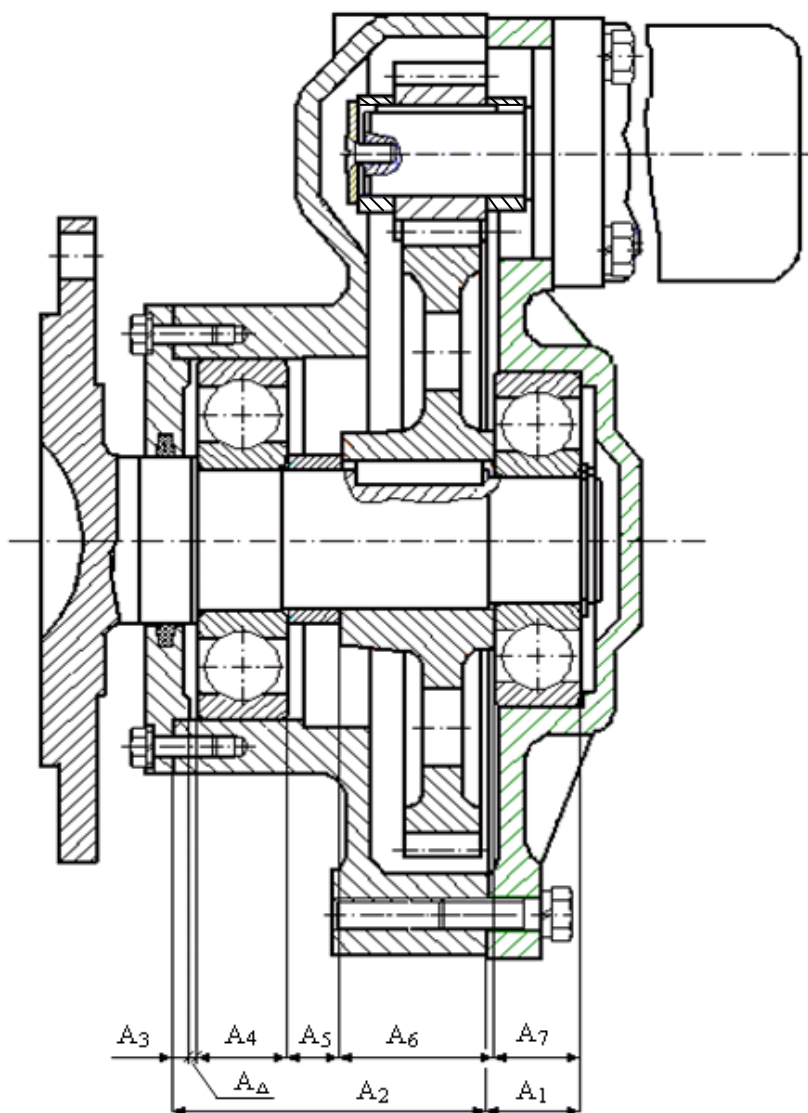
Чертеж редуктора и схема размерной цепи
